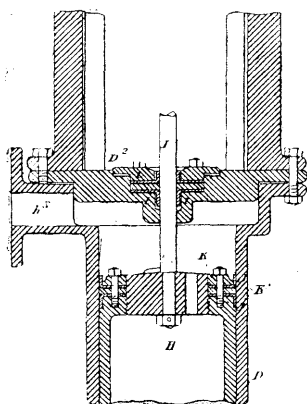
Moteur Woodbury. — Garniture du piston moteur et de sa tige — A, piston moteur à garniture de cuirs emboutis K. I, tige de ce piston, à garniture de cuirs emboutis i , serrés en D_2 . h_3 , tuyau faisant communiquer constamment le haut des deux cylindres moteurs D.
